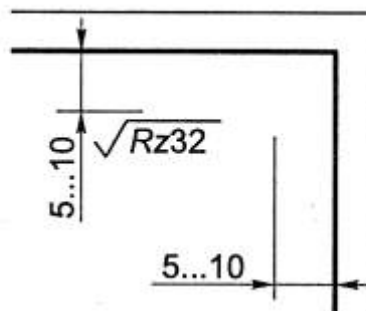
Обозначение шероховатости, когда все поверхности имеют одинаковую шероховатость
